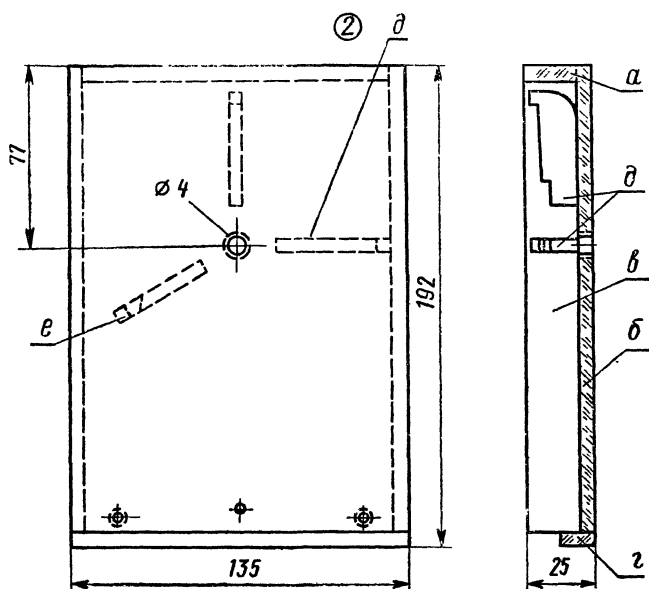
Корпус кассеты: а — задняя стенка; б — крышка; в — боковая стенка; г — передняя стенка; д, е — фигурные планки
